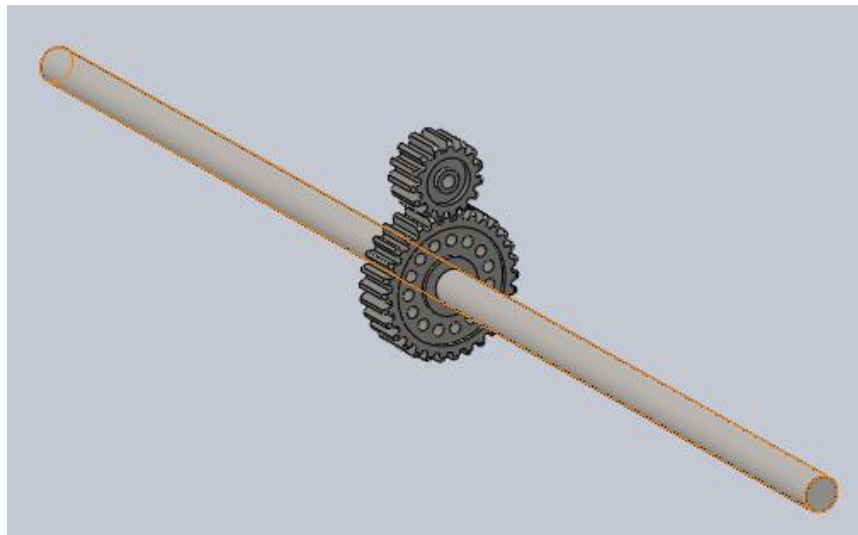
Eje de transmisión acoplado al sistema de engranajes
